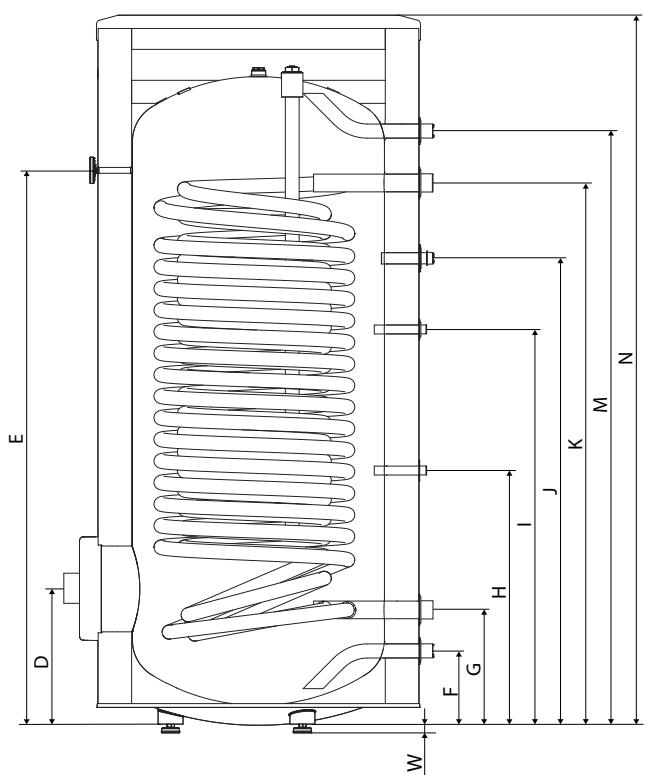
Dimensioner på BA-ST 9040/9050 - 1FEDC varmtvandsbeholder
